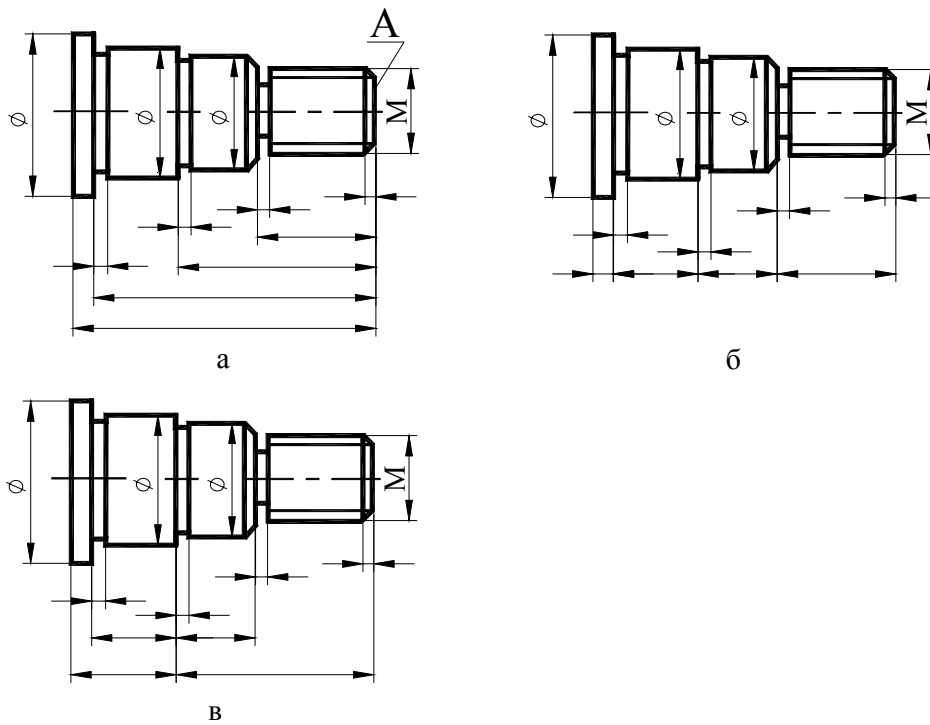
Способы задания размеров на чертежах деталей: а – координатный; б – цепной; в – комбинированный
